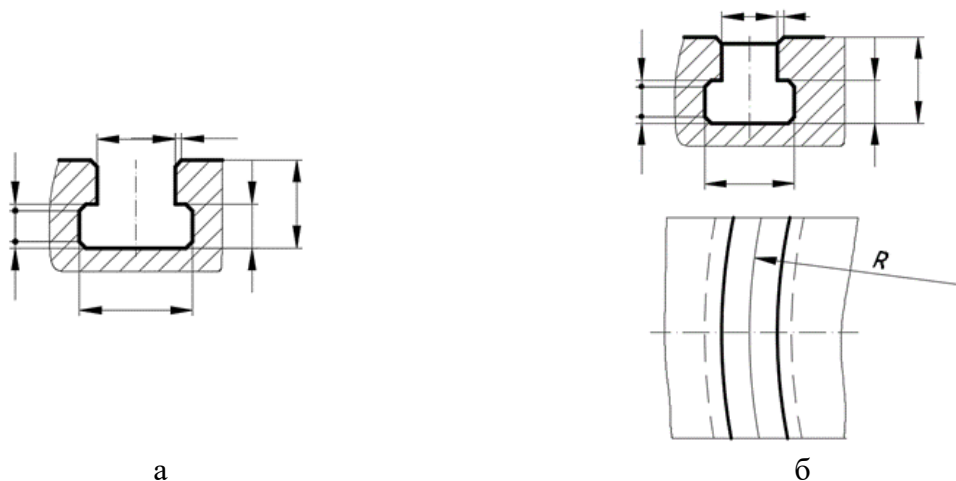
Образец выполнения чертежа Т-образных пазов.
